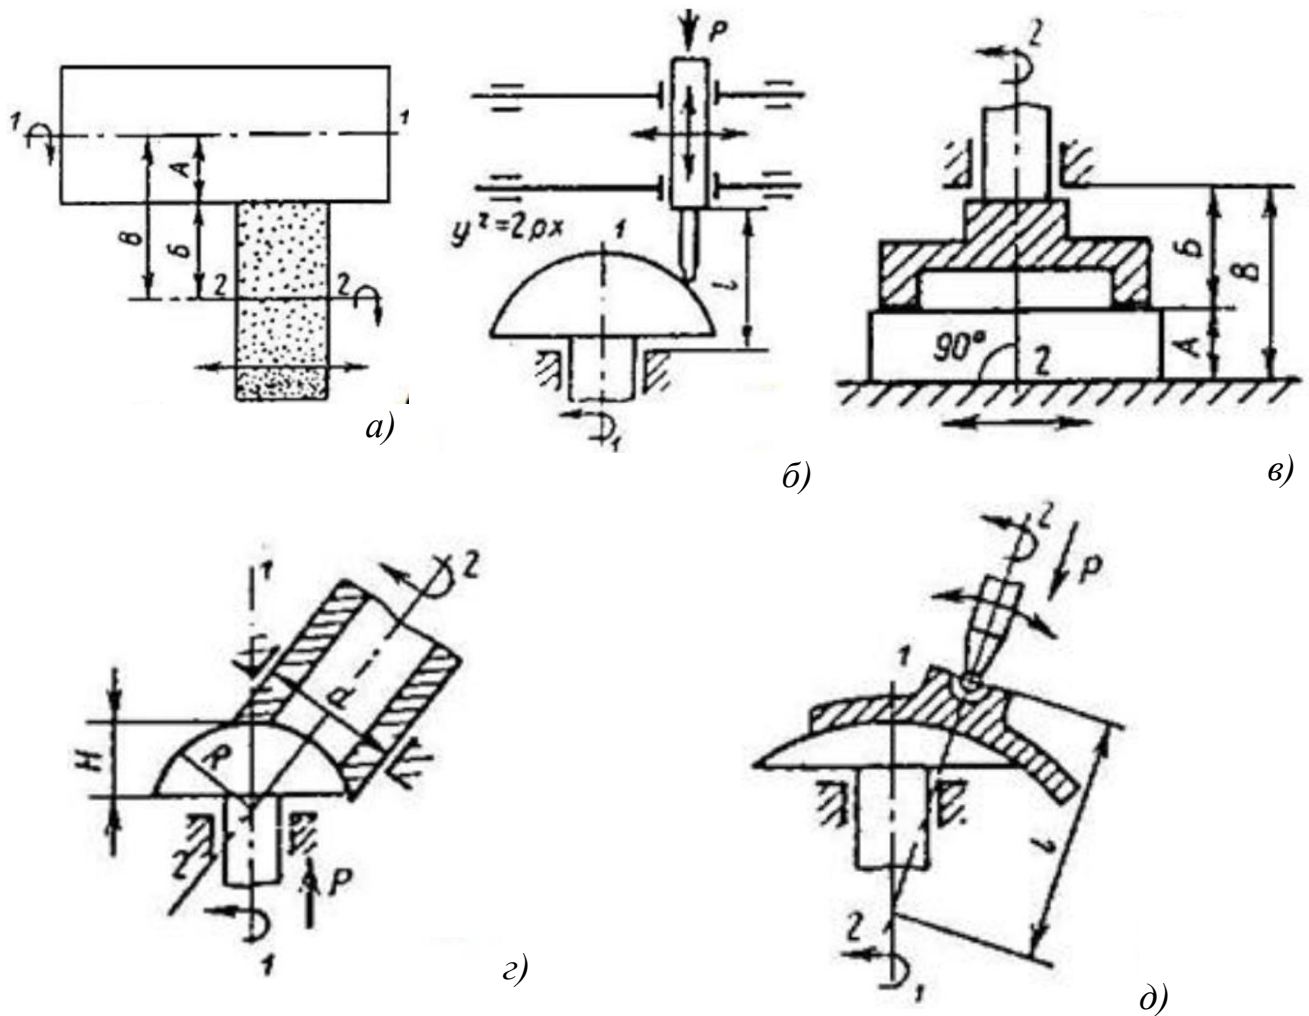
Системи ВПД обробки деталей із скла та оптичних деталей
